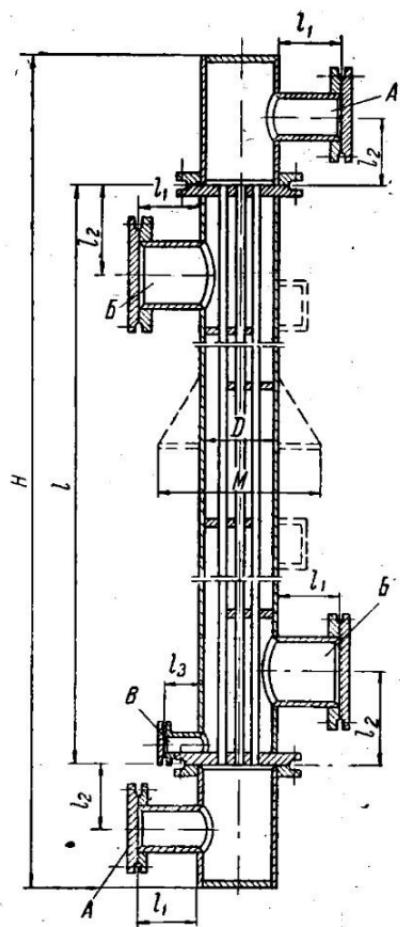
Одноходовой теплообменный аппарат типа ТН с диаметром корпуса 159 или 273 мм, имеющий две камерные сварные крышки с плоскими донышками.
